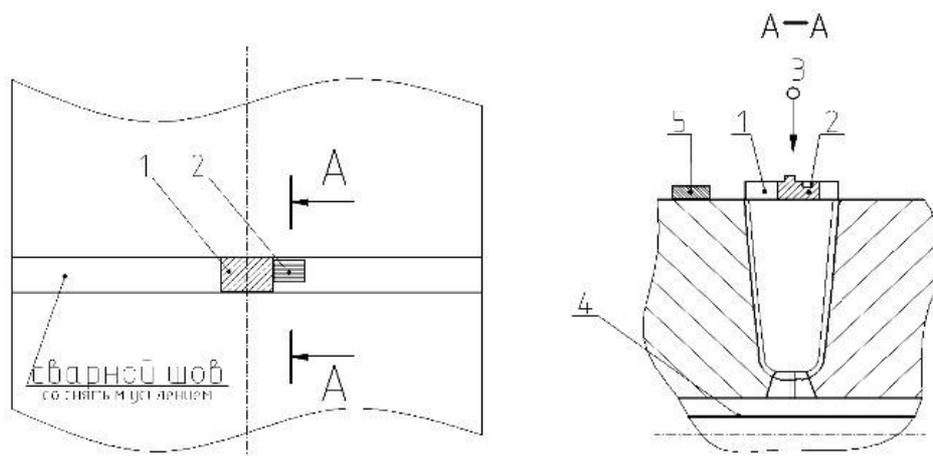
Схема контроля утяжки и проплава корня сварного шва со снятым валиком усиления:
